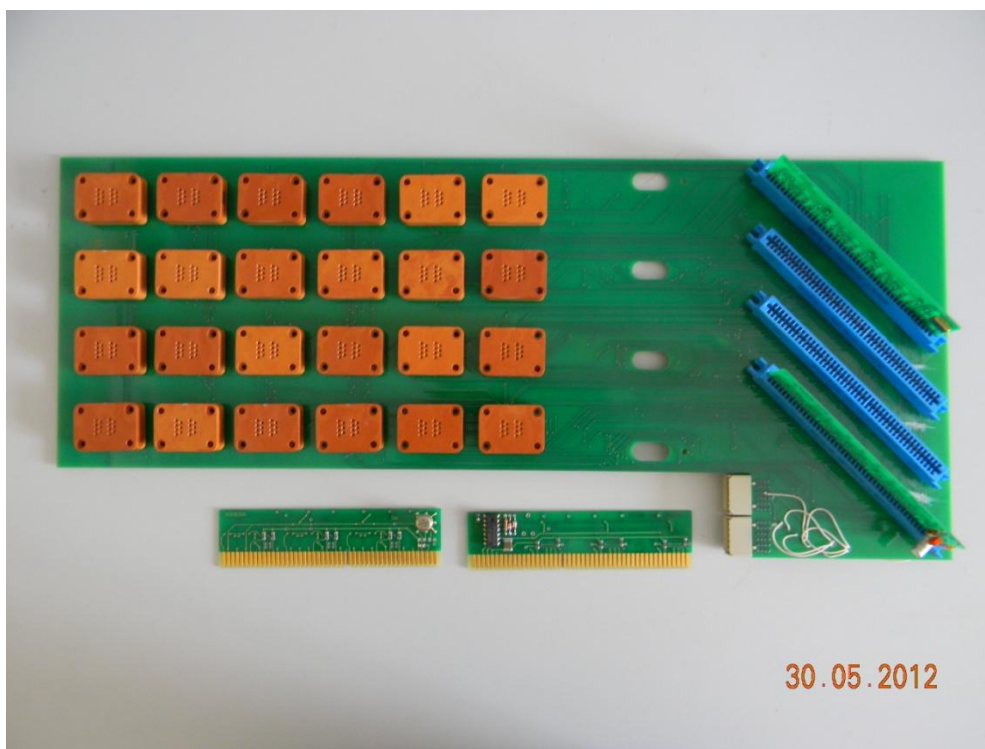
Универсальная испытательная плата со сменными нагрузками
